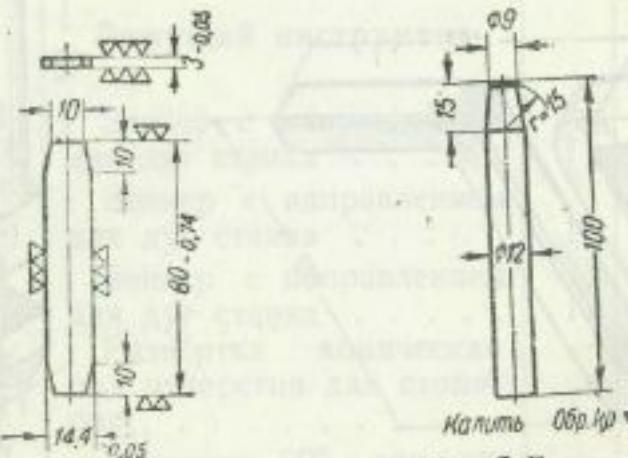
Оправка для пазов прицельного хомутника Д-ПП ПМ-8. Ст. 6, ГОСТ 380-41.
